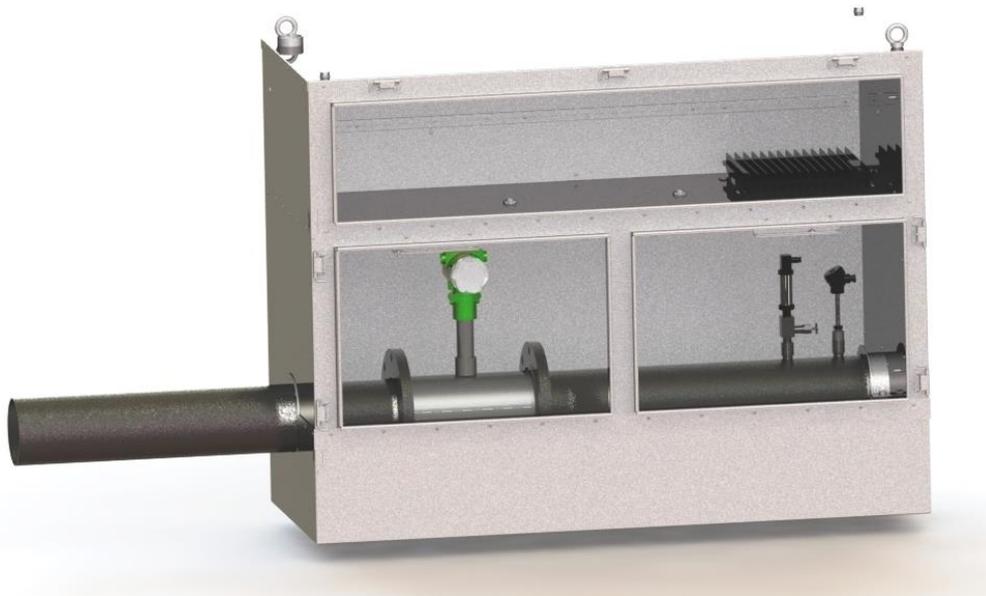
Шкаф трубный обогреваемый ШТО вертикального типа
